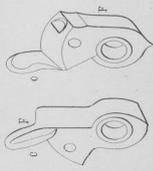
Coupe, le coup parti. — Trajet de l'extracteur.
